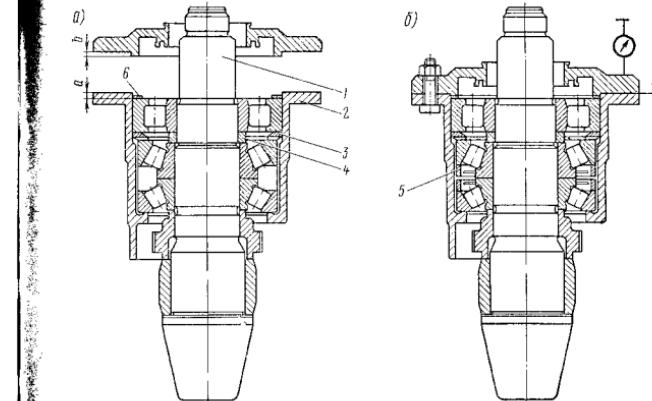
Регулировка зазоров в подшипниках и контроль осевых люфтов ведущей конической шестерни:
